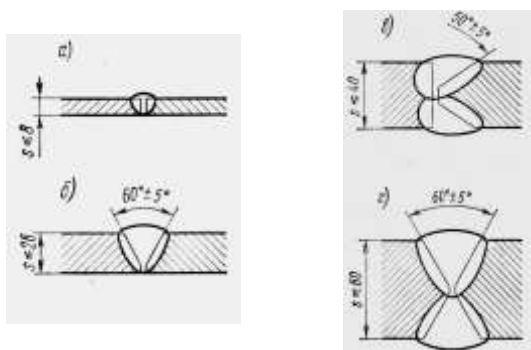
Стыковые швы: а – односторонний без скоса кромок; б - односторонний со скосом кромок; в – двусторонний с двумя симметричными скосами одной кромки; г - двусторонний с двумя симметричными скосами двух кромок
